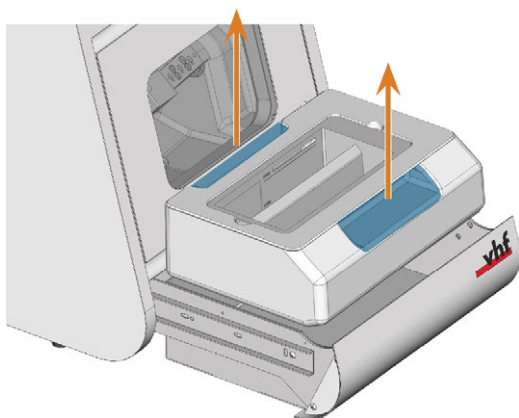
RETIRAR EL DEPÓSITO DE LÍQUIDO REFRIGERANTE DEL CAJÓN DE LÍQUIDO REFRIGERANTE
